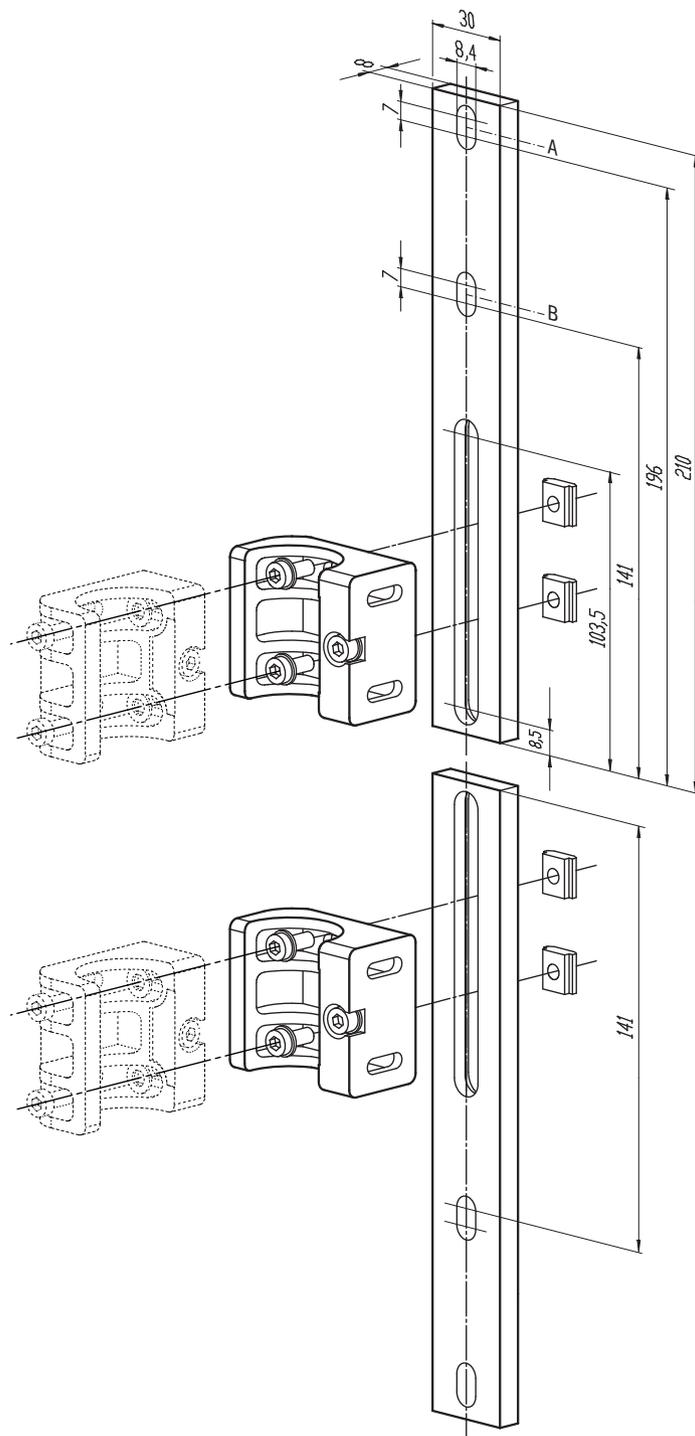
Габаритный чертеж сменного крепления (2071021)
